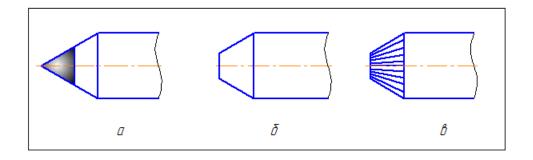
Виды рабочих поверхностей центров: а – гладкая; б – срезанная, в – с ленточками
